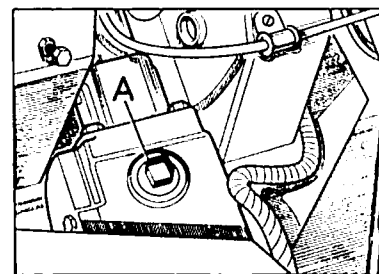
Tapón de llenado de la caja de engranajes de la dirección
